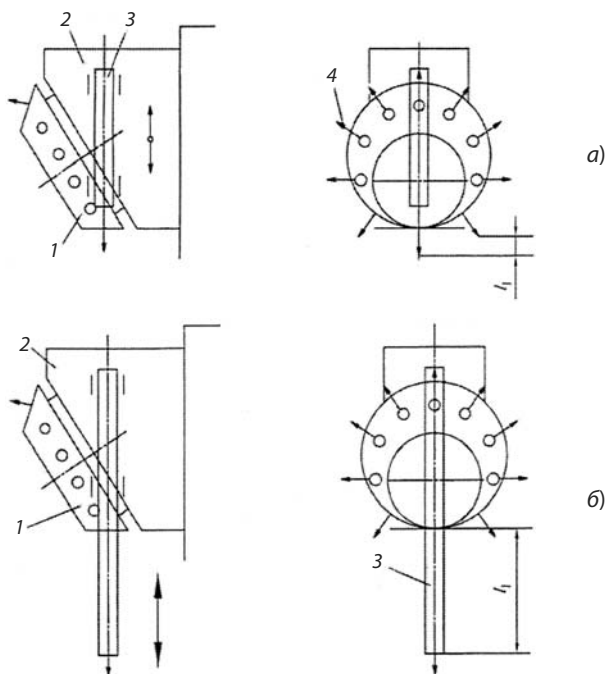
Схемы револьверных головок, применяемых на фрезерных и многоцелевых станках:
